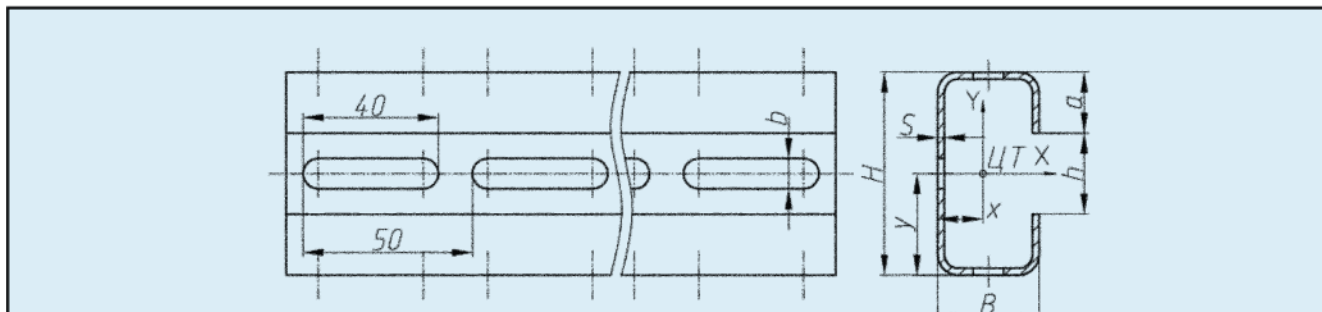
Профиль С-образный типа ПС1. Общий вид.
